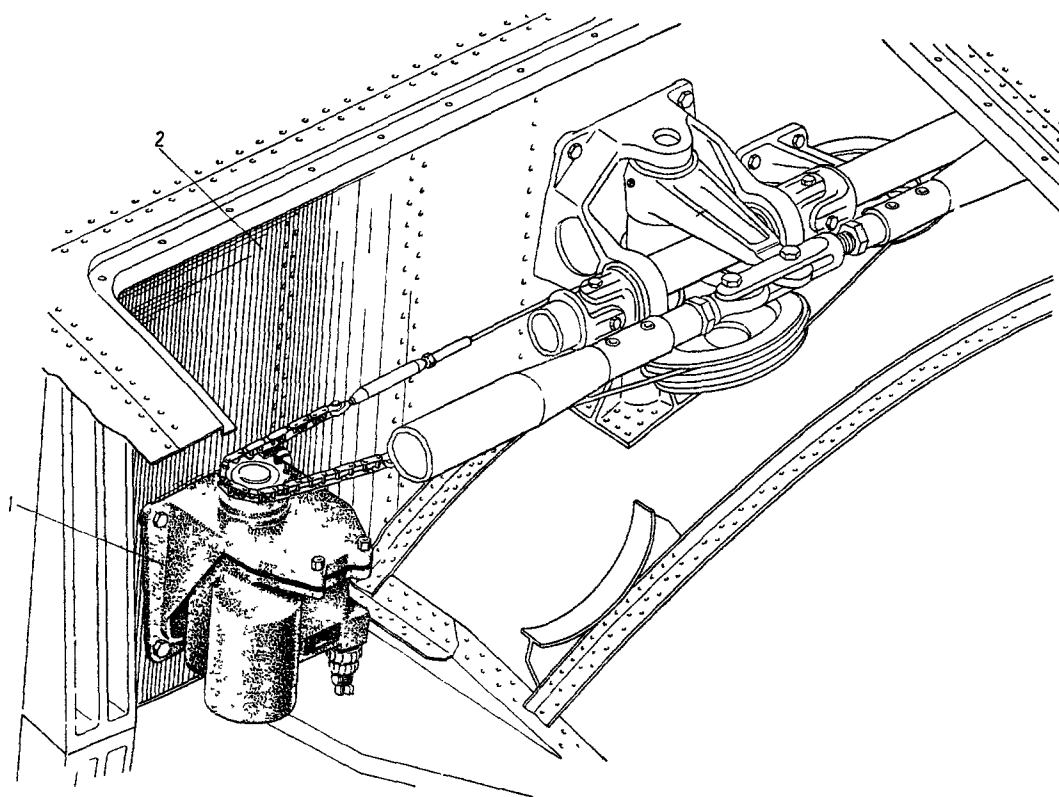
Установка рулевых машин рулей высоты и направления:
